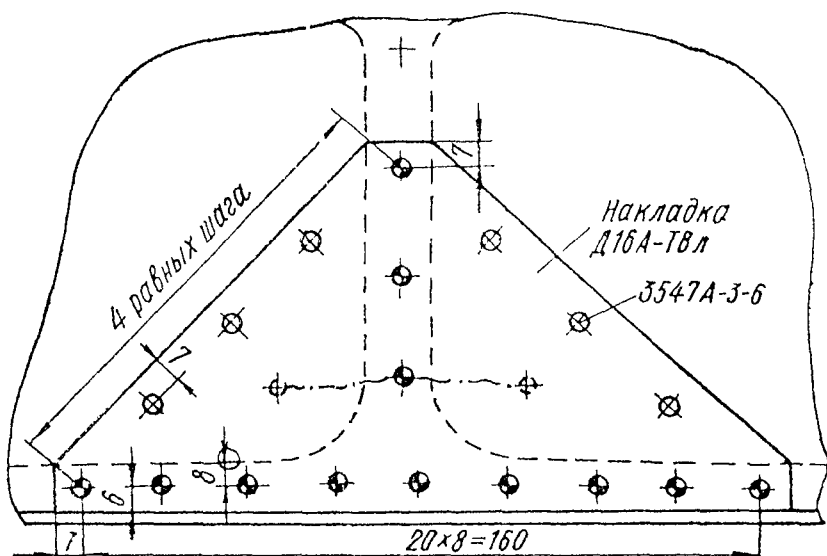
Ремонт обшивки установкой накладки сверху обшивки
